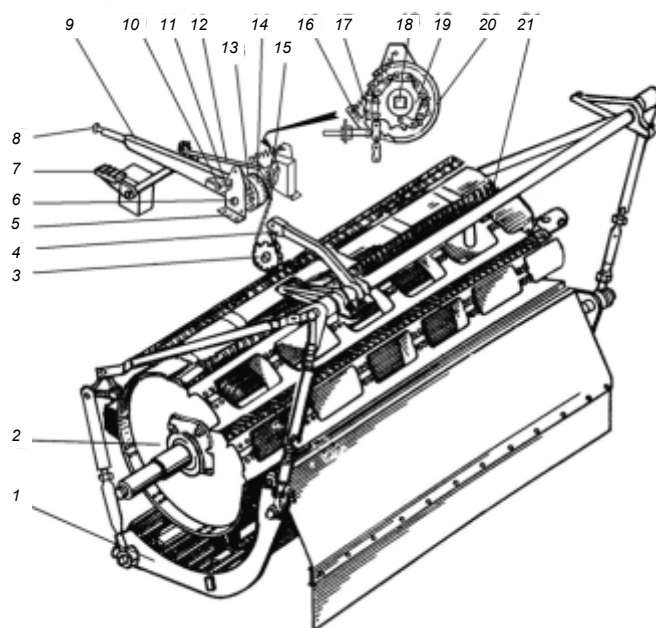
Механизм регулировки подбарабанья зерноуборочного комбайна КЗС-7 «Палессе GS07»:
